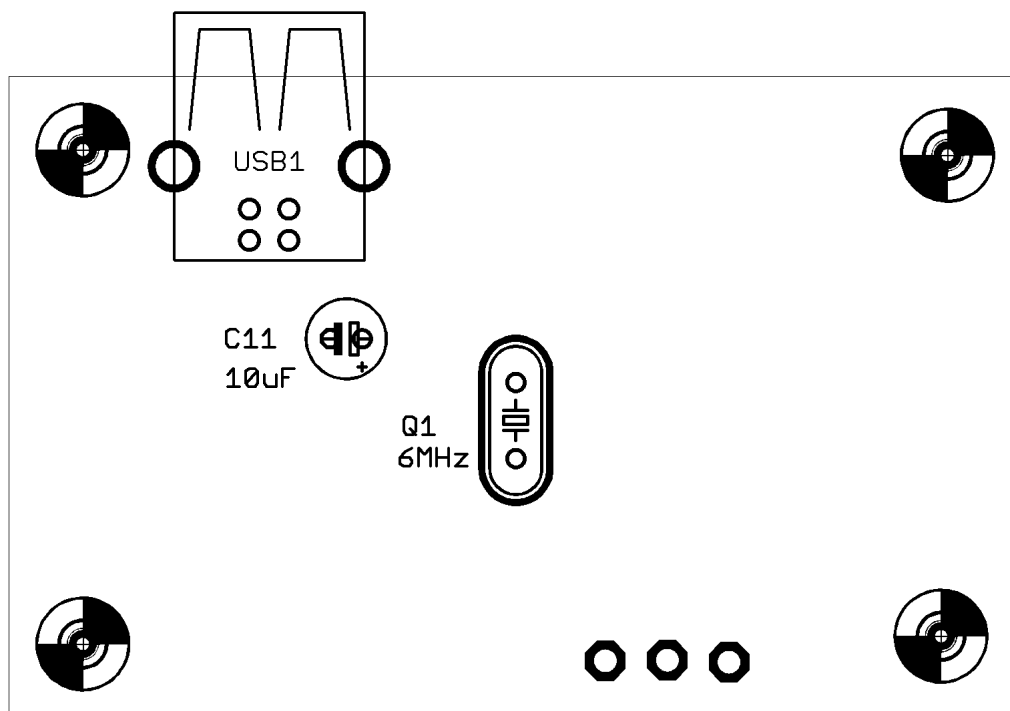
Deska plošného spoje (skutečný rozměr je 40x65mm)
